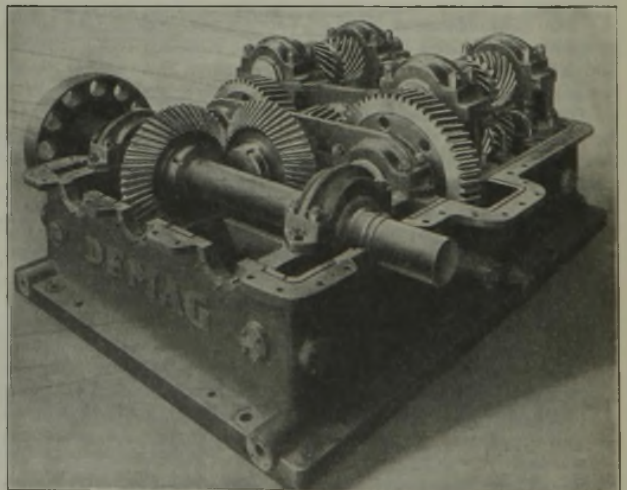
Getriebe von Walzgerüsten einer kontinuierlichen Drahtstraße.
